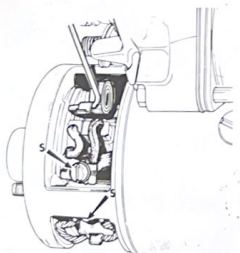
Parte trasera del motor de arranque sin la abrazadera de inspección.
